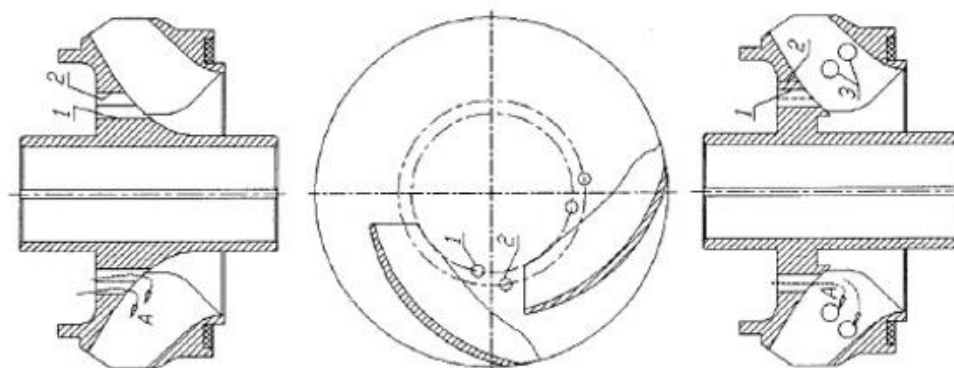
Рабочие колеса диспергатора типа AGH
